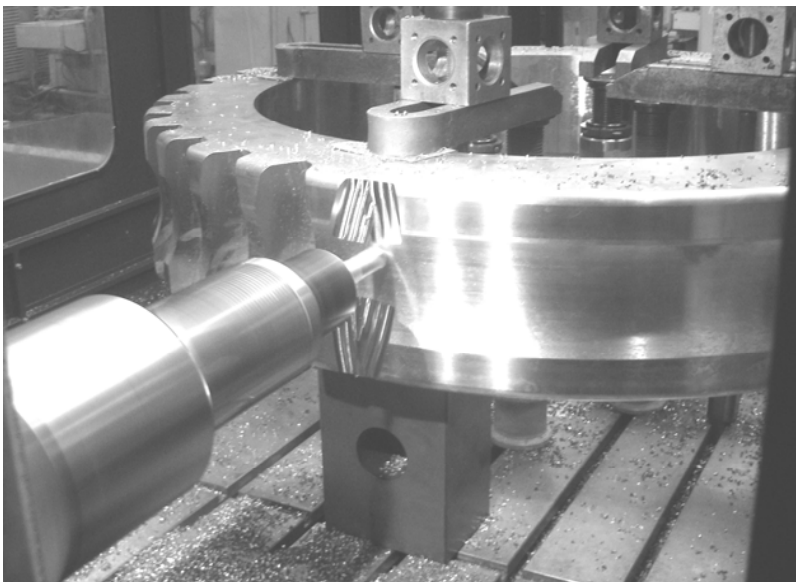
Нарезка зубьев червячного колеса на станке с ЧПУ "TOS VARNSDORF"
